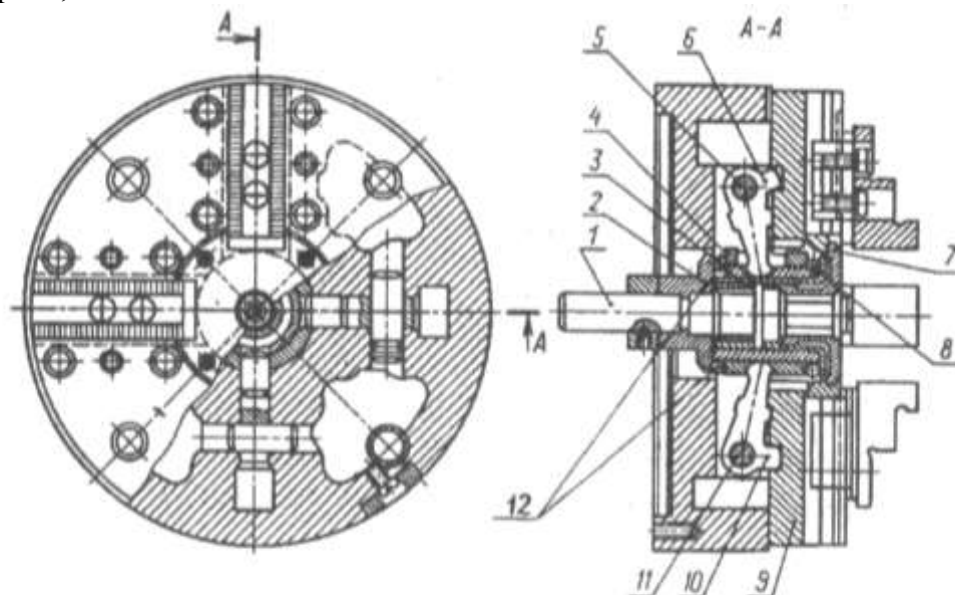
Универсальный четырехкулачковый патрон с механизированным приводом
